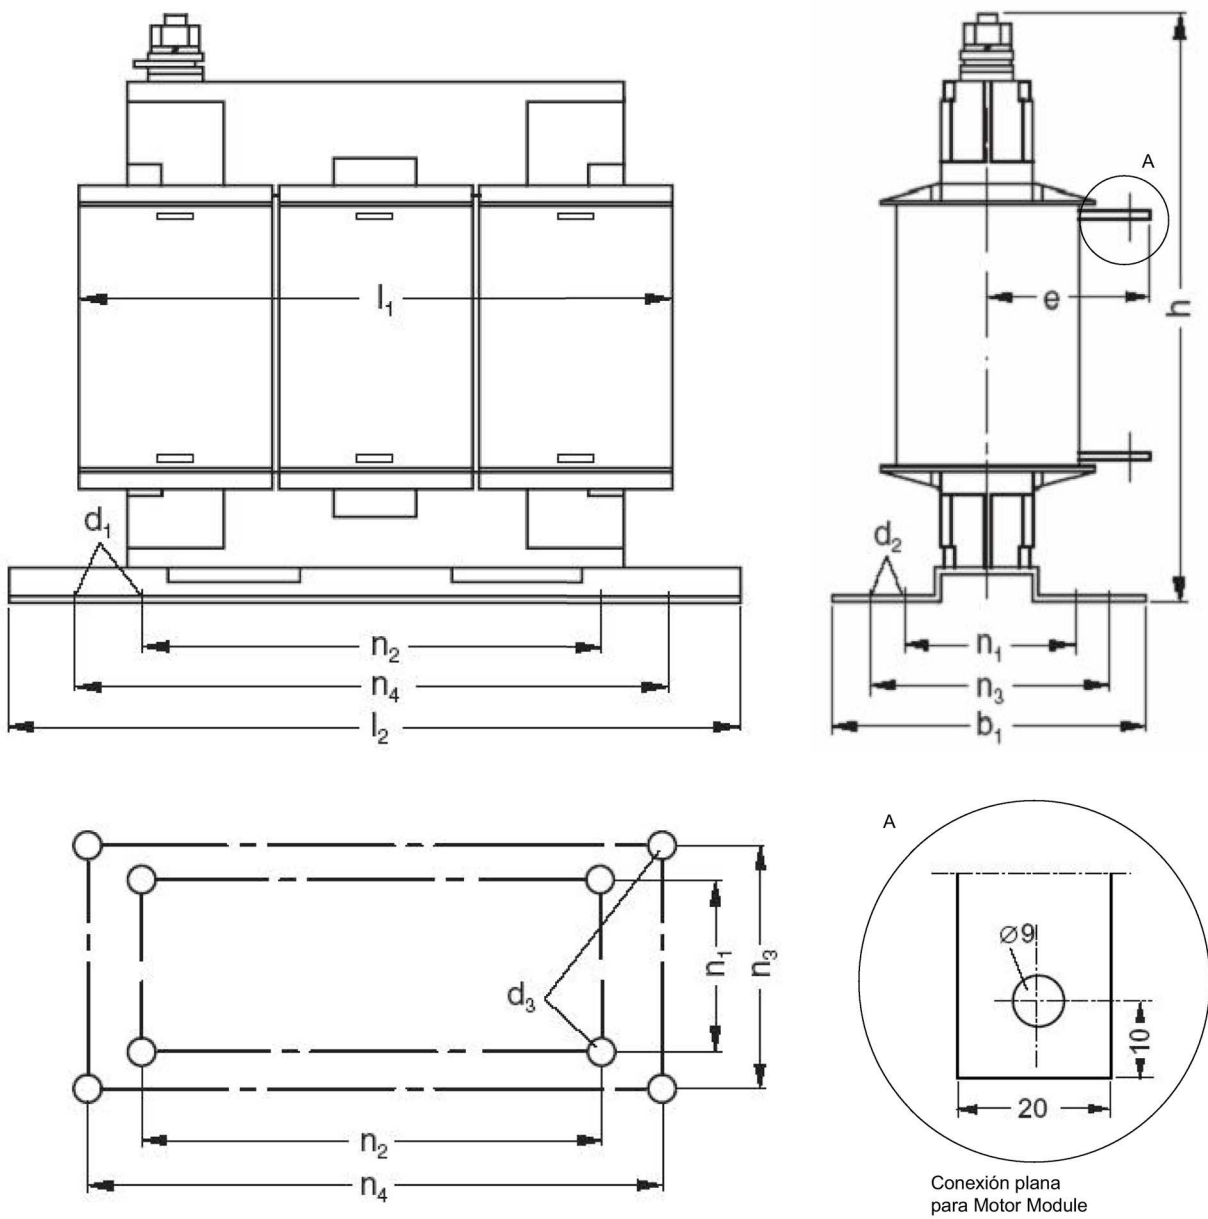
Croquis acotado y orificio de montaje de la bobina de motor de 60 A (6SL3000-2BE26-0AA0)
